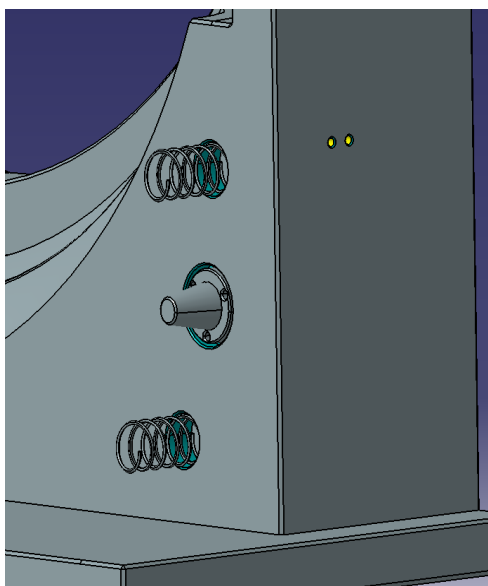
Zhloubení pro uložení rozevíracích pružin
